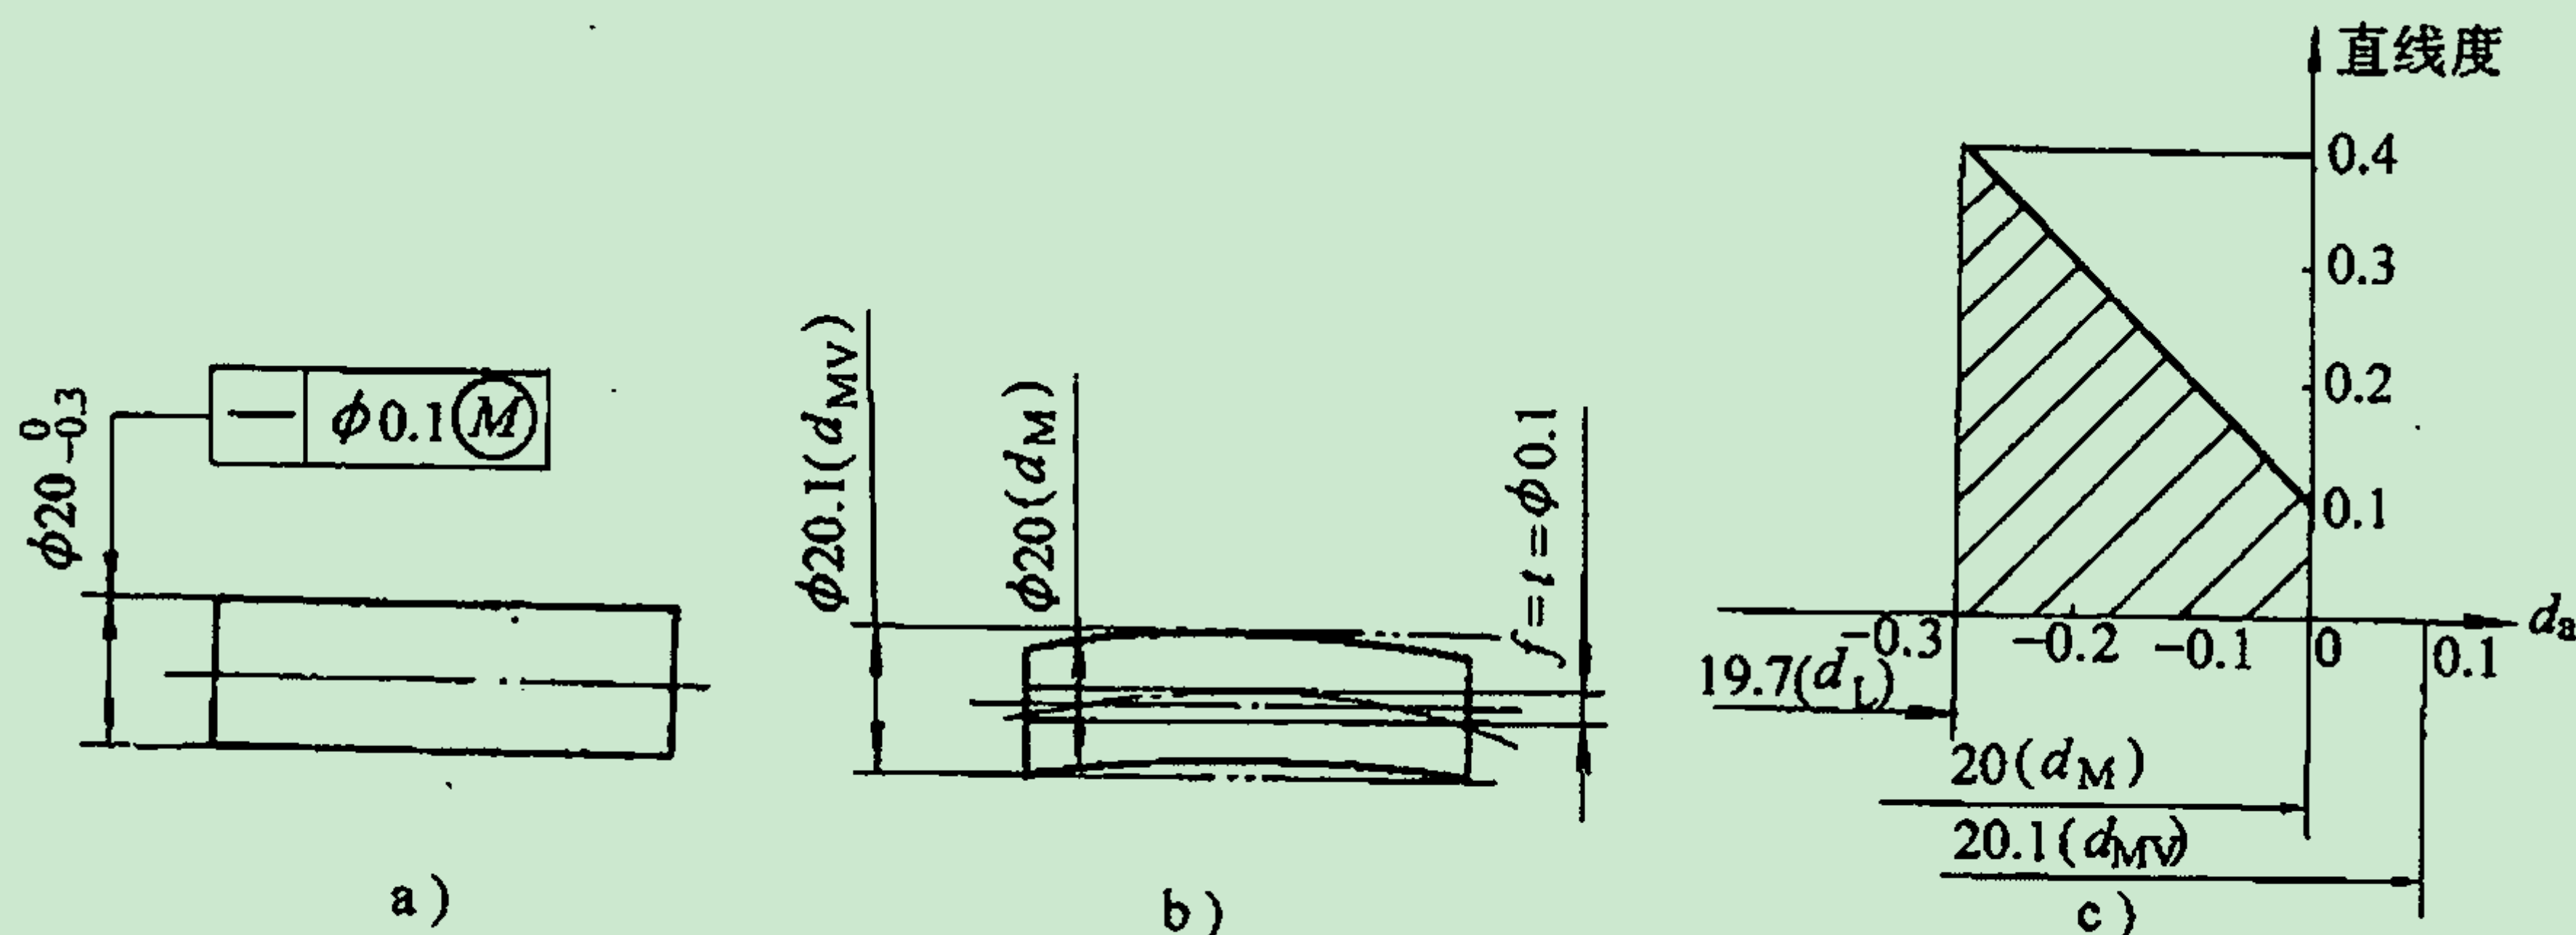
轴线直线度公差采用最大实体要求
